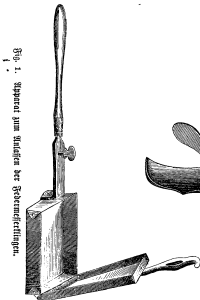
Werkzeug zum Schleifen der Federmetallschneide.
